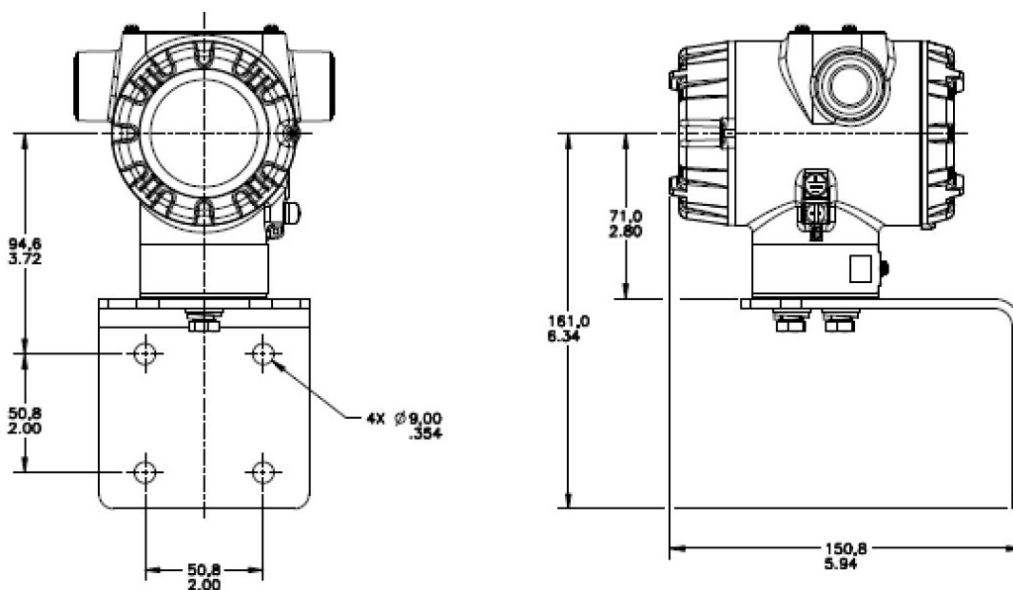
STT750 без адаптера. Монтаж на вертикальную трубу при помощи угловой монтажной скобы
